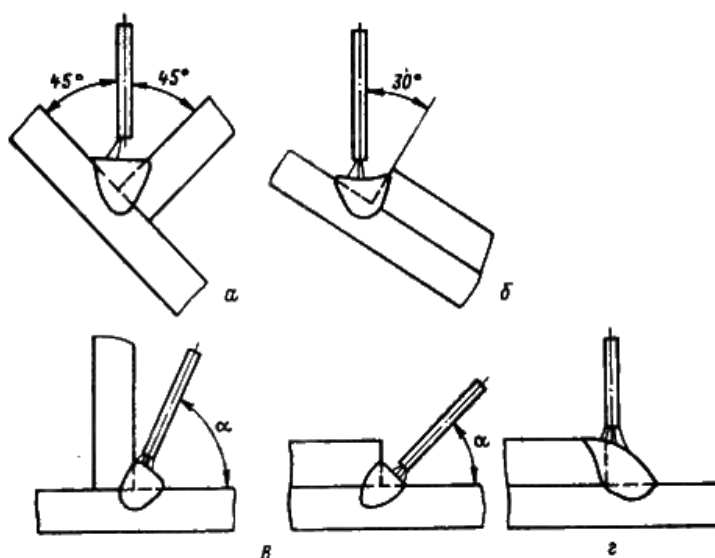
Основні схеми автоматичного зварювання під флюсом
